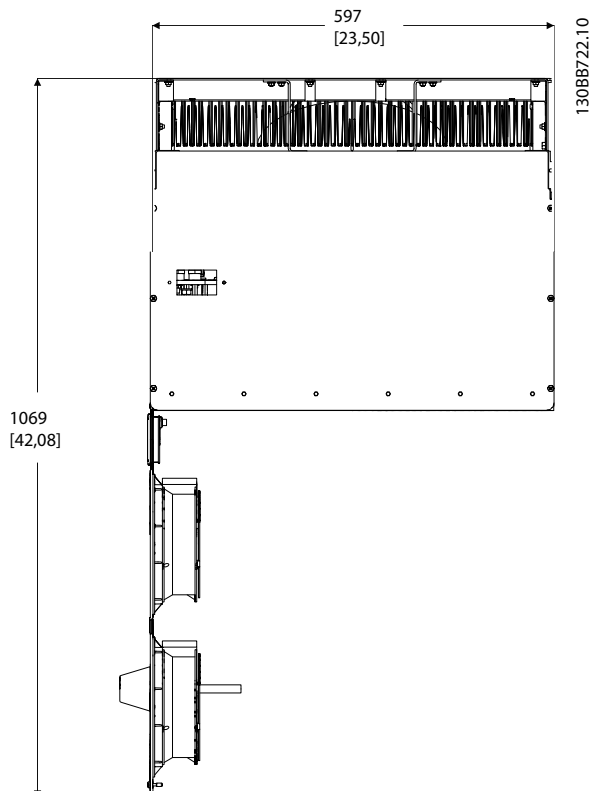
Platz vor Gehäuse-Typ IP21/IP54, Baugröße E9.
